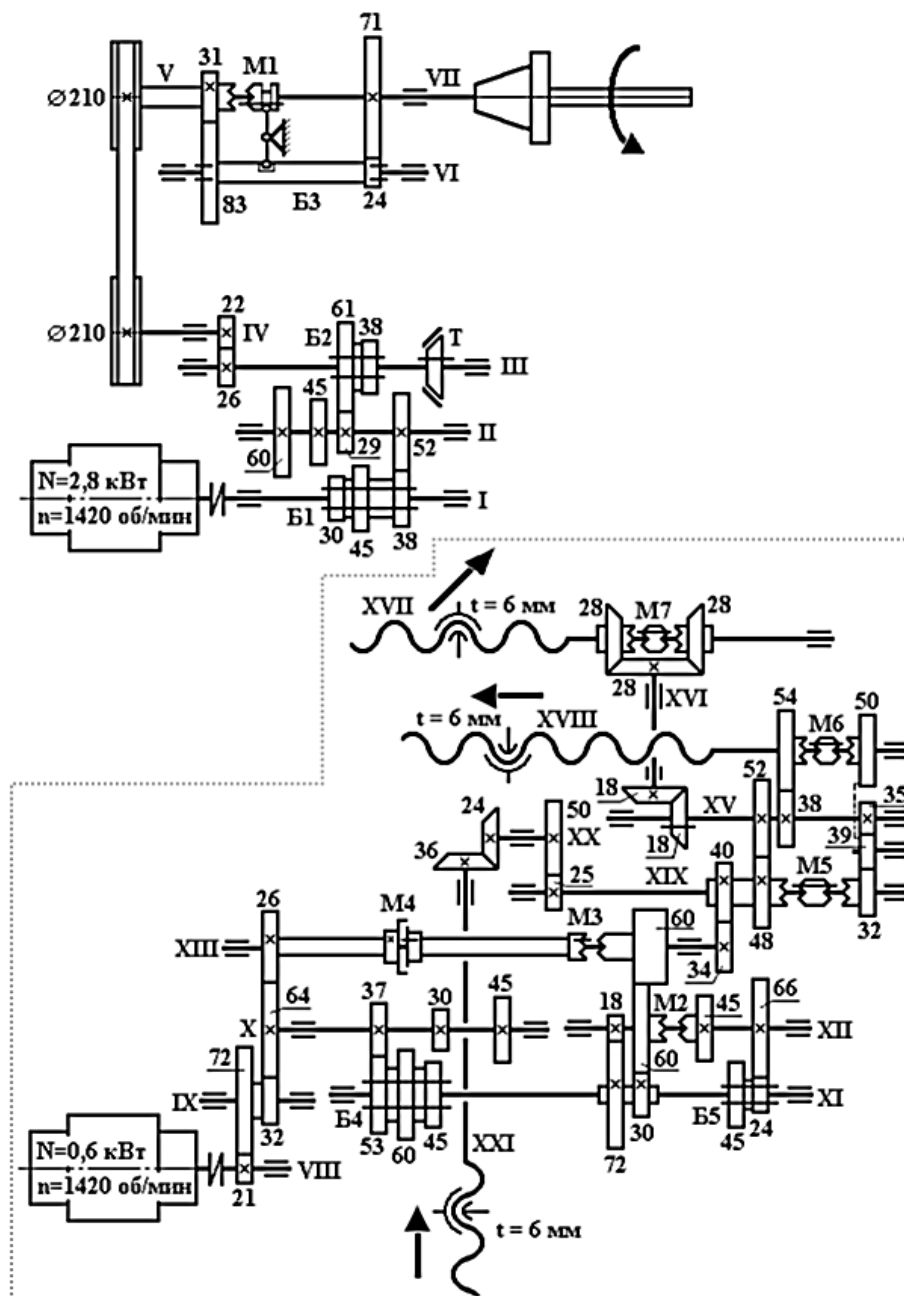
Кинематическая схема горизонтально-фрезерного станка модели 6М80Г (в пунктирный контур заключена цепь движения подачи)
